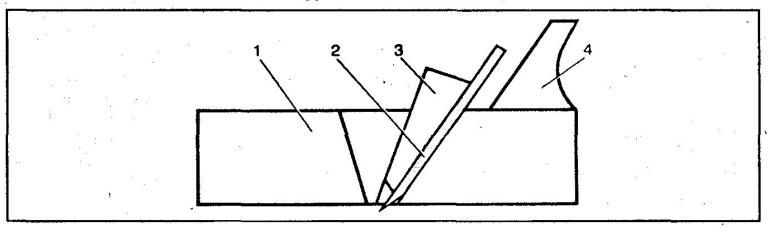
Устройство рубанка: I – колодка; 2 – нож; 3 – клин; 4 – ручка
